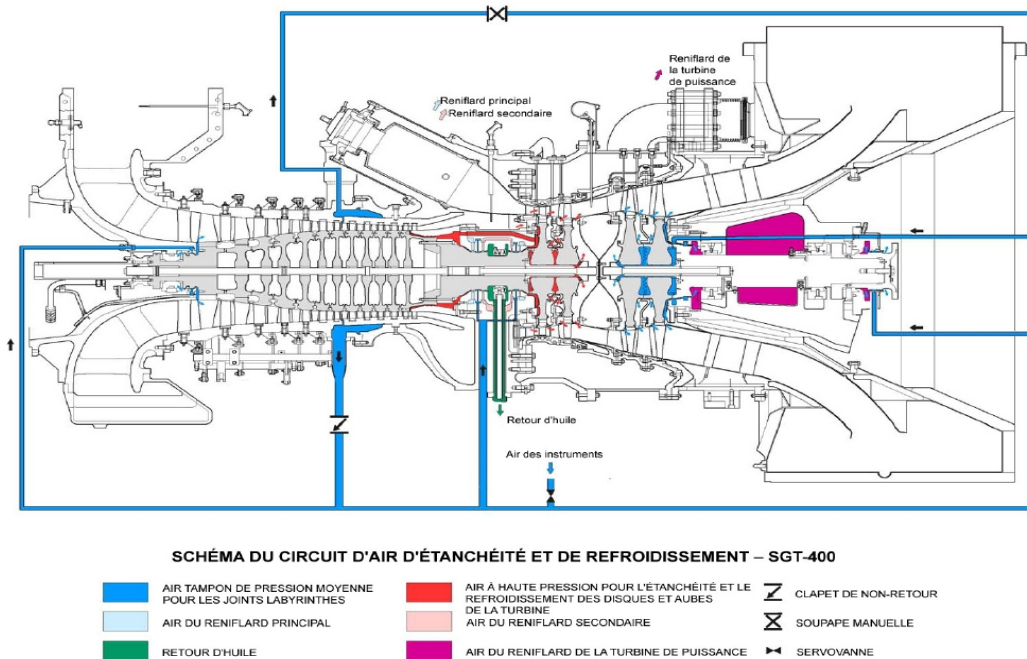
Système d'air de refroidissement et d'étanchéité^[10].
